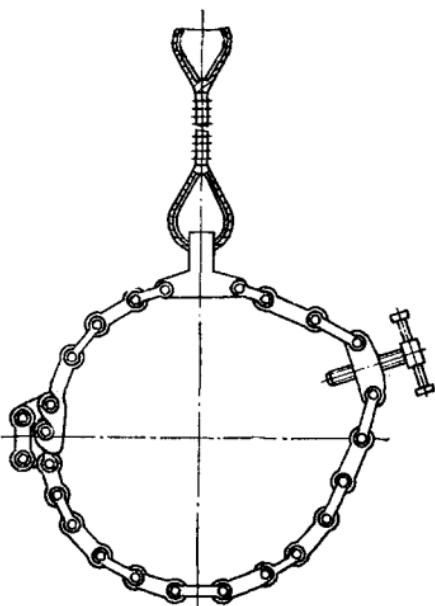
Приспособление для установки и транспортировки деталей (грузоподъемностью 500 кг)
